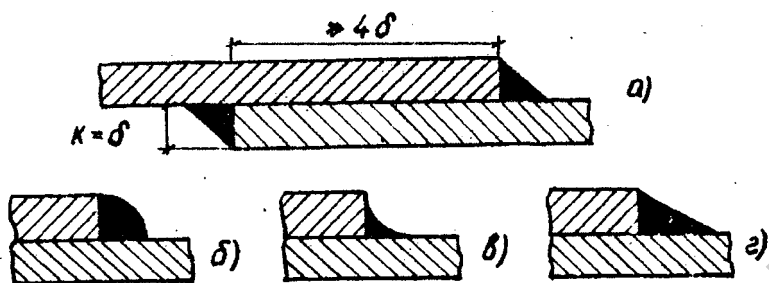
Виды нахлесточных сварных соединений
